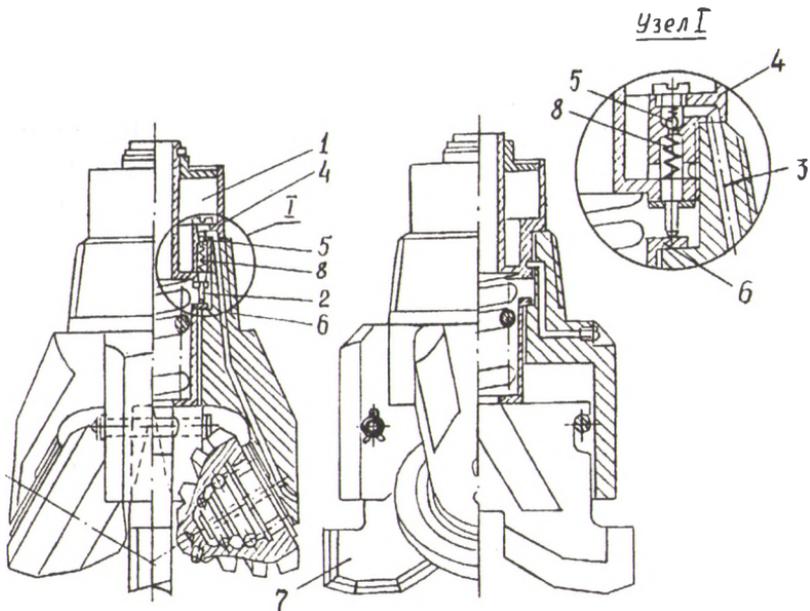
Режуще-шарошечное долото ИрГТУ с устройством для подачи смазки в опоры шарошек
